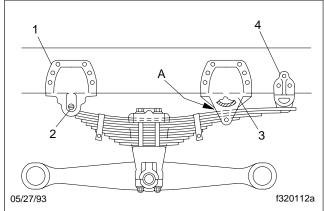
, Connexion d'extrémité du balancier de type adaptateur à trois pièces
